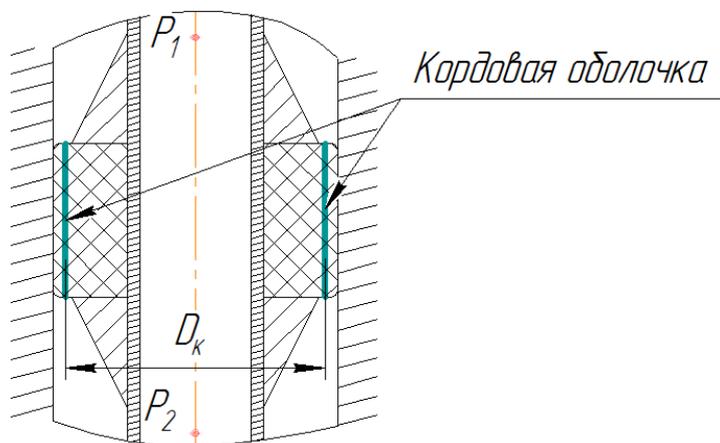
Резиновый уплотнительный элемент с кордовой оболочкой в распакерованном положении
